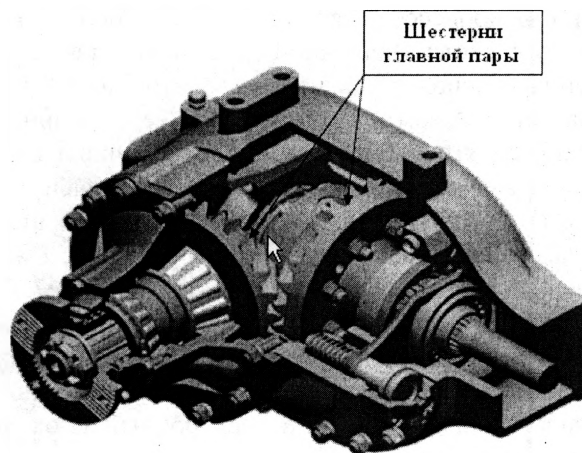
Внешний вид центрального редуктора заднего моста автомобиля МАЗ
